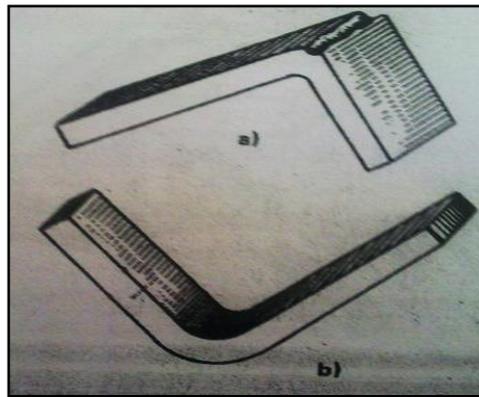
Defectos del doblado. a) Desgarradura; b) Reducido del metal
